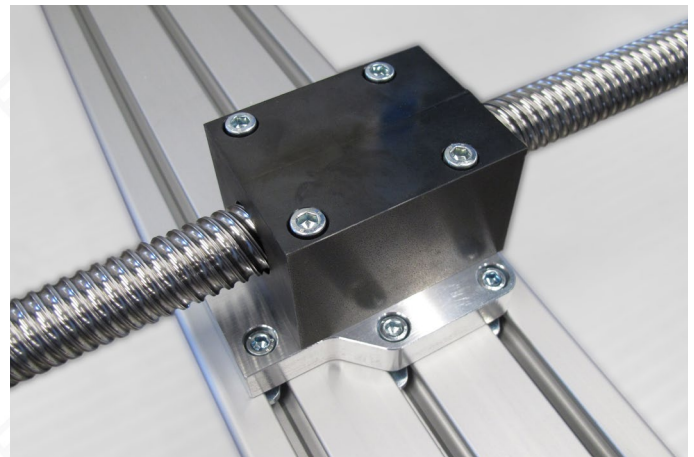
Mittelspindel mit Kugelumlaufmutter und Flanschplatte
